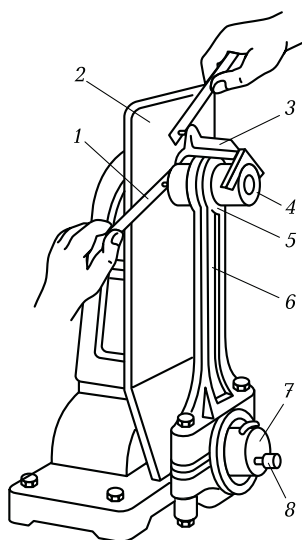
Приспособление для контроля прямолинейности шатуна:
